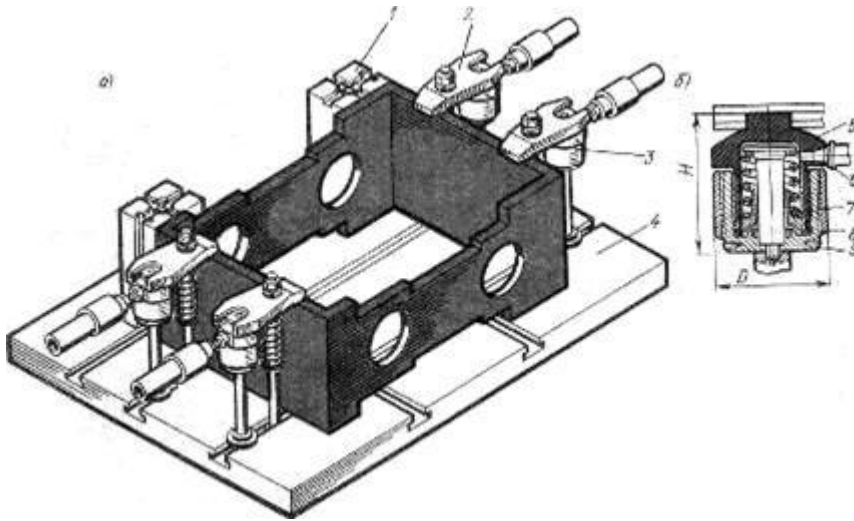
Пристосування з елементів УСПМ-ЧПУ : а - загальне компонування; б - гідроциліндр прихвата.
